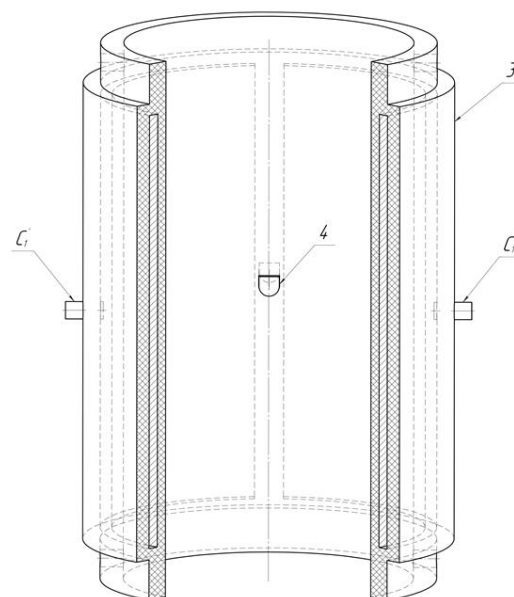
Общий вид конструкции полуцилиндрического ёмкостного датчика-дозатора
